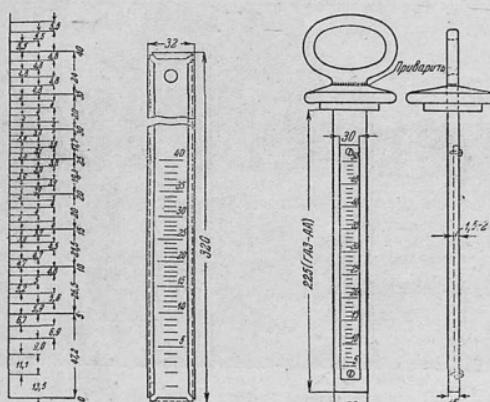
Линейка для замера бензина. Слева — разметка шкалы линейки для автомобилей ГАЗ-АА
